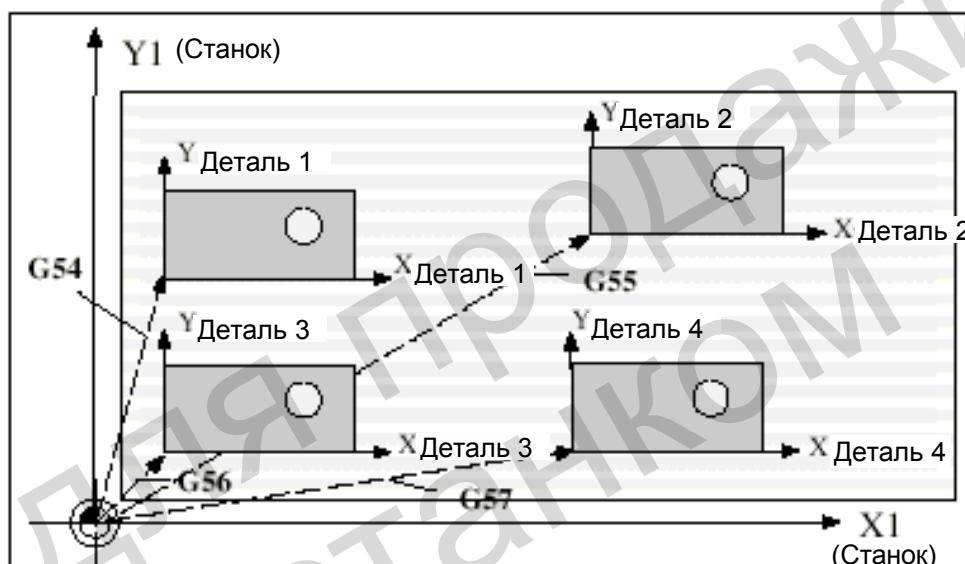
Несколько зажимов детали при сверлении/фрезеровании
